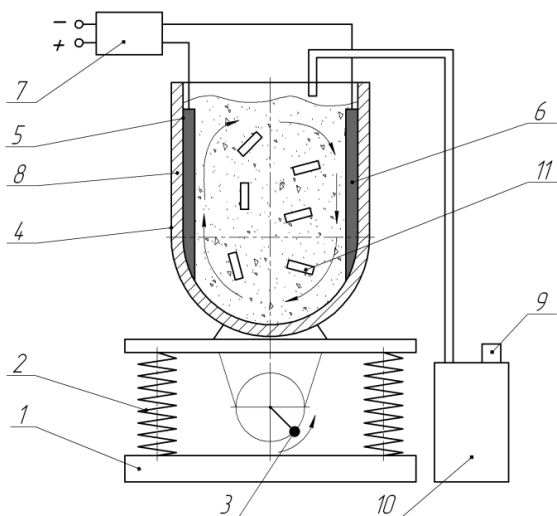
Схема электрохимической виброобработки: 1 – основание; 2 – упругая подвеска; 3 – вибровозбудитель; 4 – резервуар; 5, 6 – электроды; 7 – источник тока; 8 – облицовка; 9 – насос; 10 – бак; 11 – обрабатываемые детали
